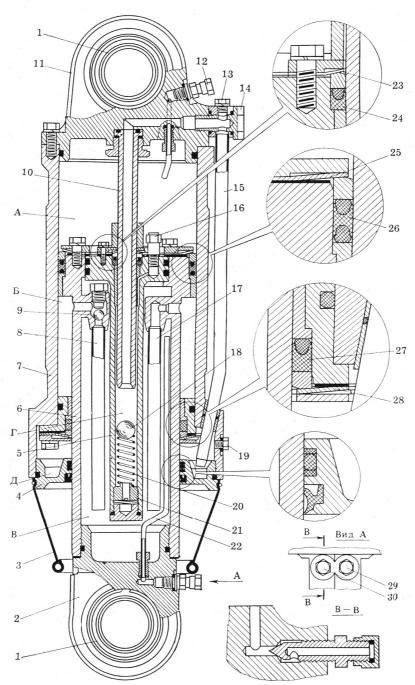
Пневмогидравлический цилиндр подвесок автомобилей БелАЗ: 1 — шарнирный подшипник; 2 — нижняя крышка; 3 — защитная муфта; 4 — крышка картера маслосборника; 5 — гильза насоса; 6 — цилиндр противодавления; 7 — основной рабочий цилиндр; 8, 17 — соединительные трубки; 9 — обратный клапан отбоя; 10 — плунжер насоса; 11 — верхняя крышка; 12, 29 — зарядные клапаны; 13 — пробка; 14 — соединительный штуцер; 15 — наружная трубка насоса; 16 — обратный клапан насоса; 18 — клапан нагнетания насоса; 19 — контрольная пробка; 20 — пружина клапана; 21 — регулировочная гайка; 22 — заправочная трубка; 23, 25, 28 — пружины нажимного устройства; 24, 26, 27 — манжетные уплотнения; 30 — заправочный штуцер; 4 — надпоршневая (верхняя) полость; 5 — подпоршневая (кольцевая) полость; 5 — подпоршневая (нижняя) полость противодавления; 5 — полость гильзы насоса; 5 — полость маслосборника
